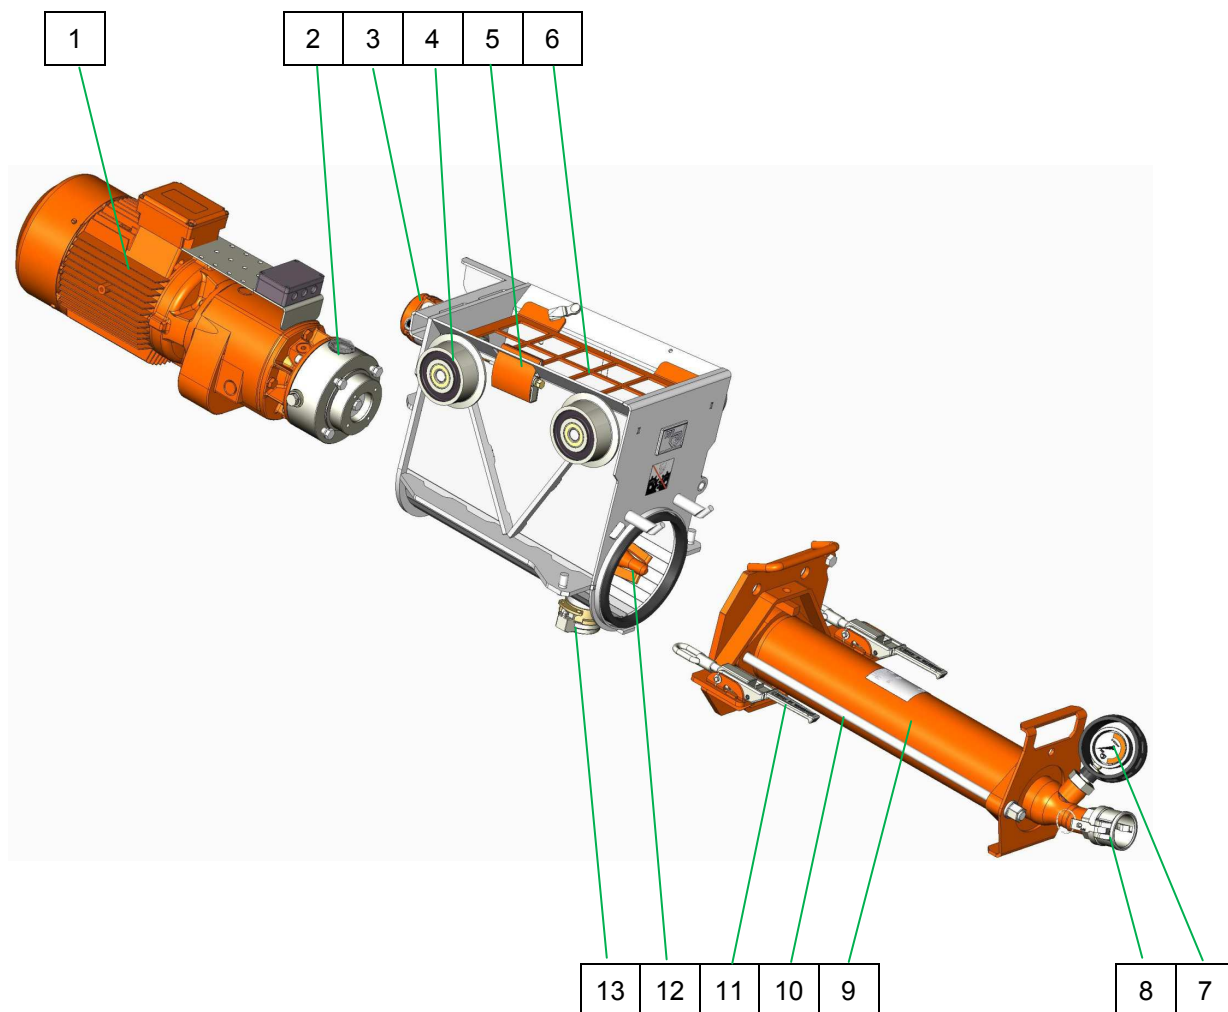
Übersicht Pumpenmotor mit Behälter und Pumpe
